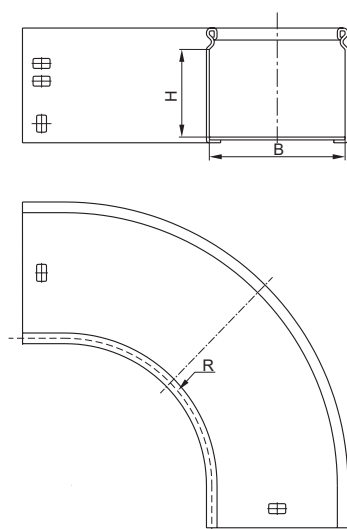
Поворот плавный 90° тип Г01. Размеры для размещения кабеля / Figure С.2 – 90° smooth bend Г01 type. Dimensions for cable placement
